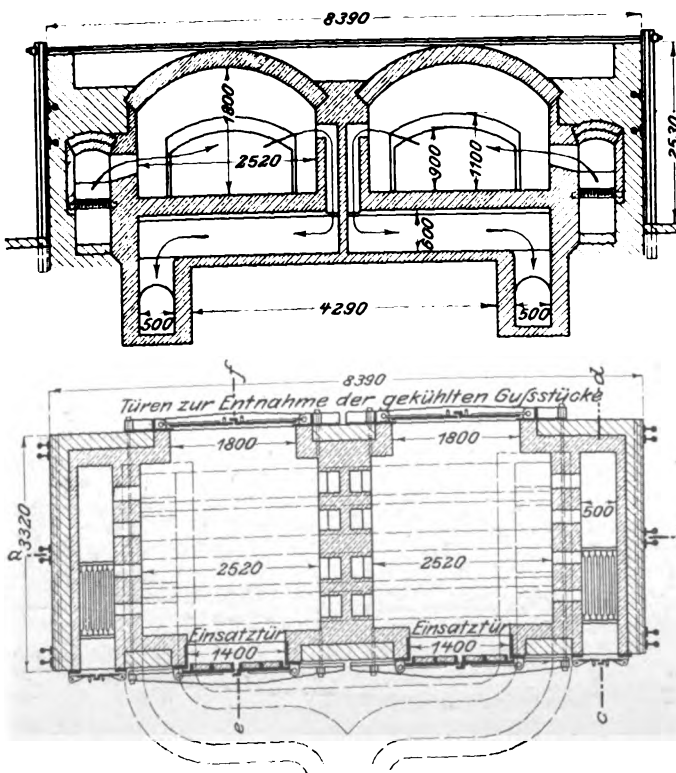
bis 9. Kühlöfen für die Gußstücke.
